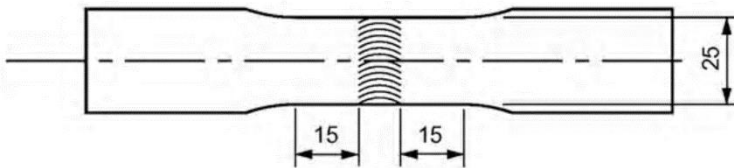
Probeta para el ensayo de tracción perpendicular a la soldadura
